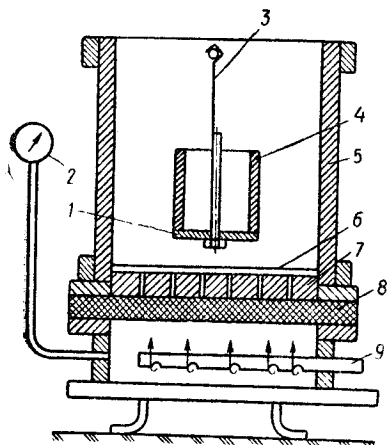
Установка для вихрового напилювання полімерного матеріалу:
